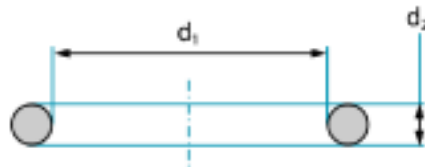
Dimensiones o-ring seleccionado 59.69 x 5.33 de la marca Trelleborg
